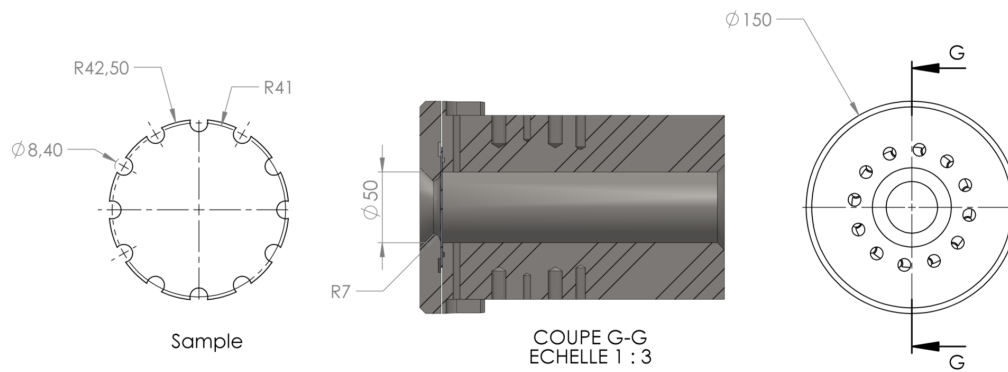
Géométries du flan et du dispositif de gonflement hydraulique (dimensions en mm)
